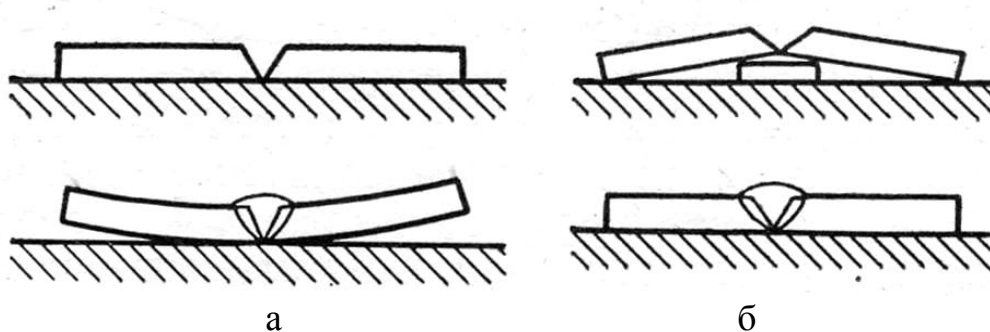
Зварювання вихідних заготовок: а – без попереднього згинання; б – з попереднім згинанням у зоні зварювання
